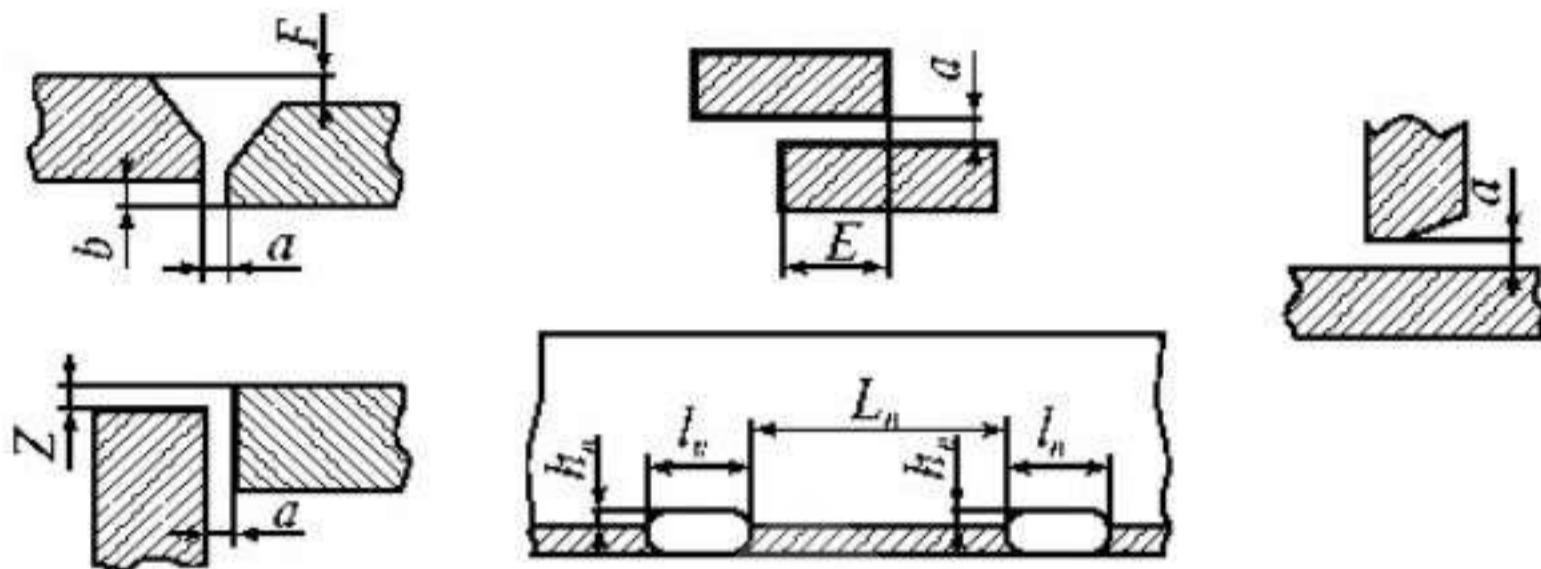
Контролируемые параметры сварных соединений
